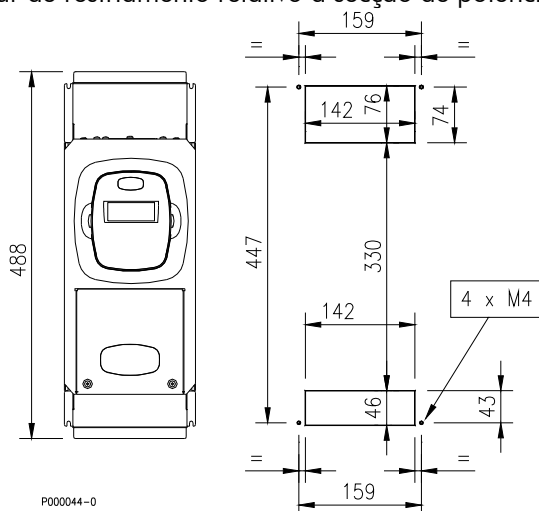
Dimensões de furação do painel para montagem passante SINUS PENTA S05
